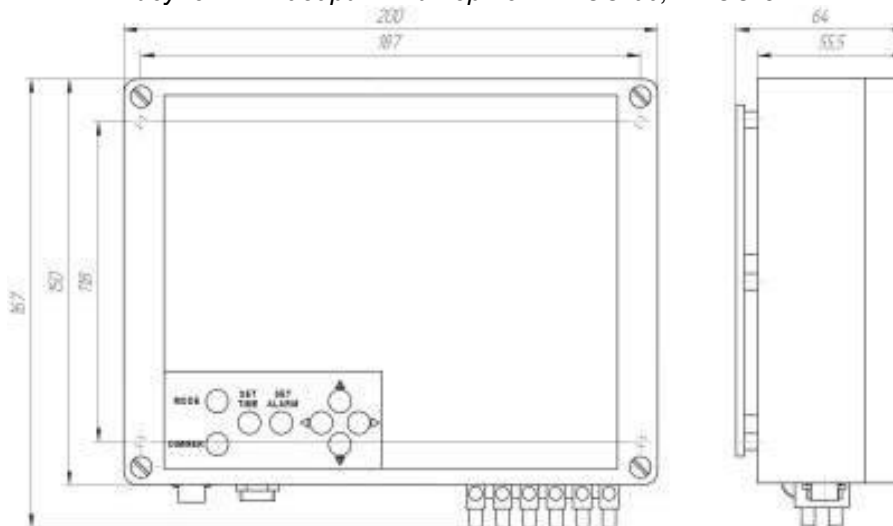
Габаритный чертеж ИПСС-02, ИПСС-03
